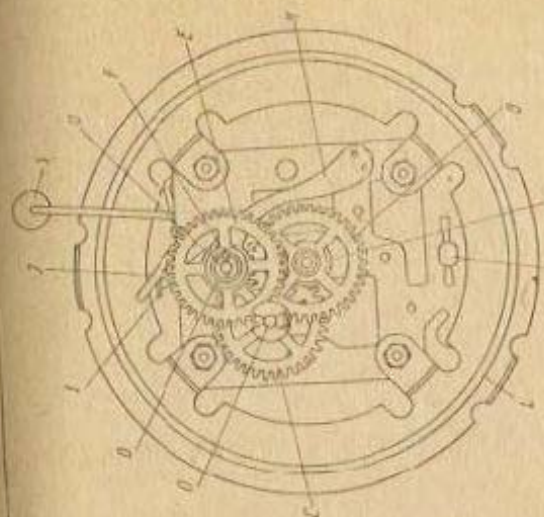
Mecanismul deșteptătorului din partea cadrului:
